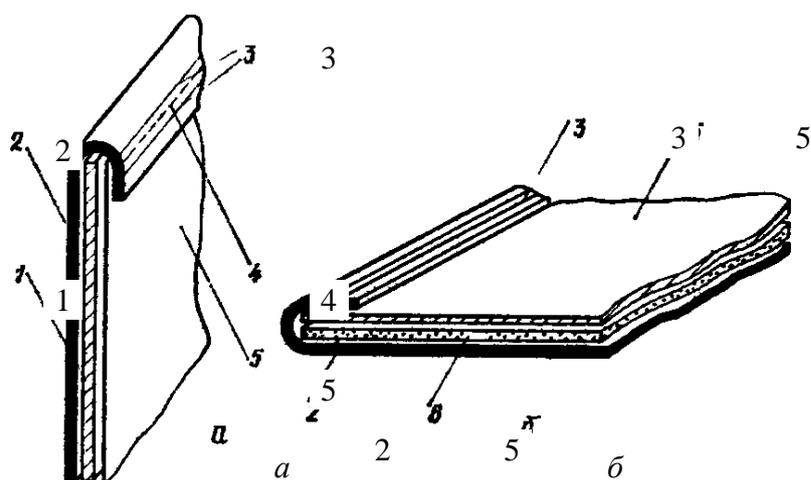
Схемы сварки деталей ТВЧ: 1— картон; 2 — искусственная кожа; 3 — сварной шов; 4—строчка; 5—ПВХ-пленка; 6 — пенополиуретан
